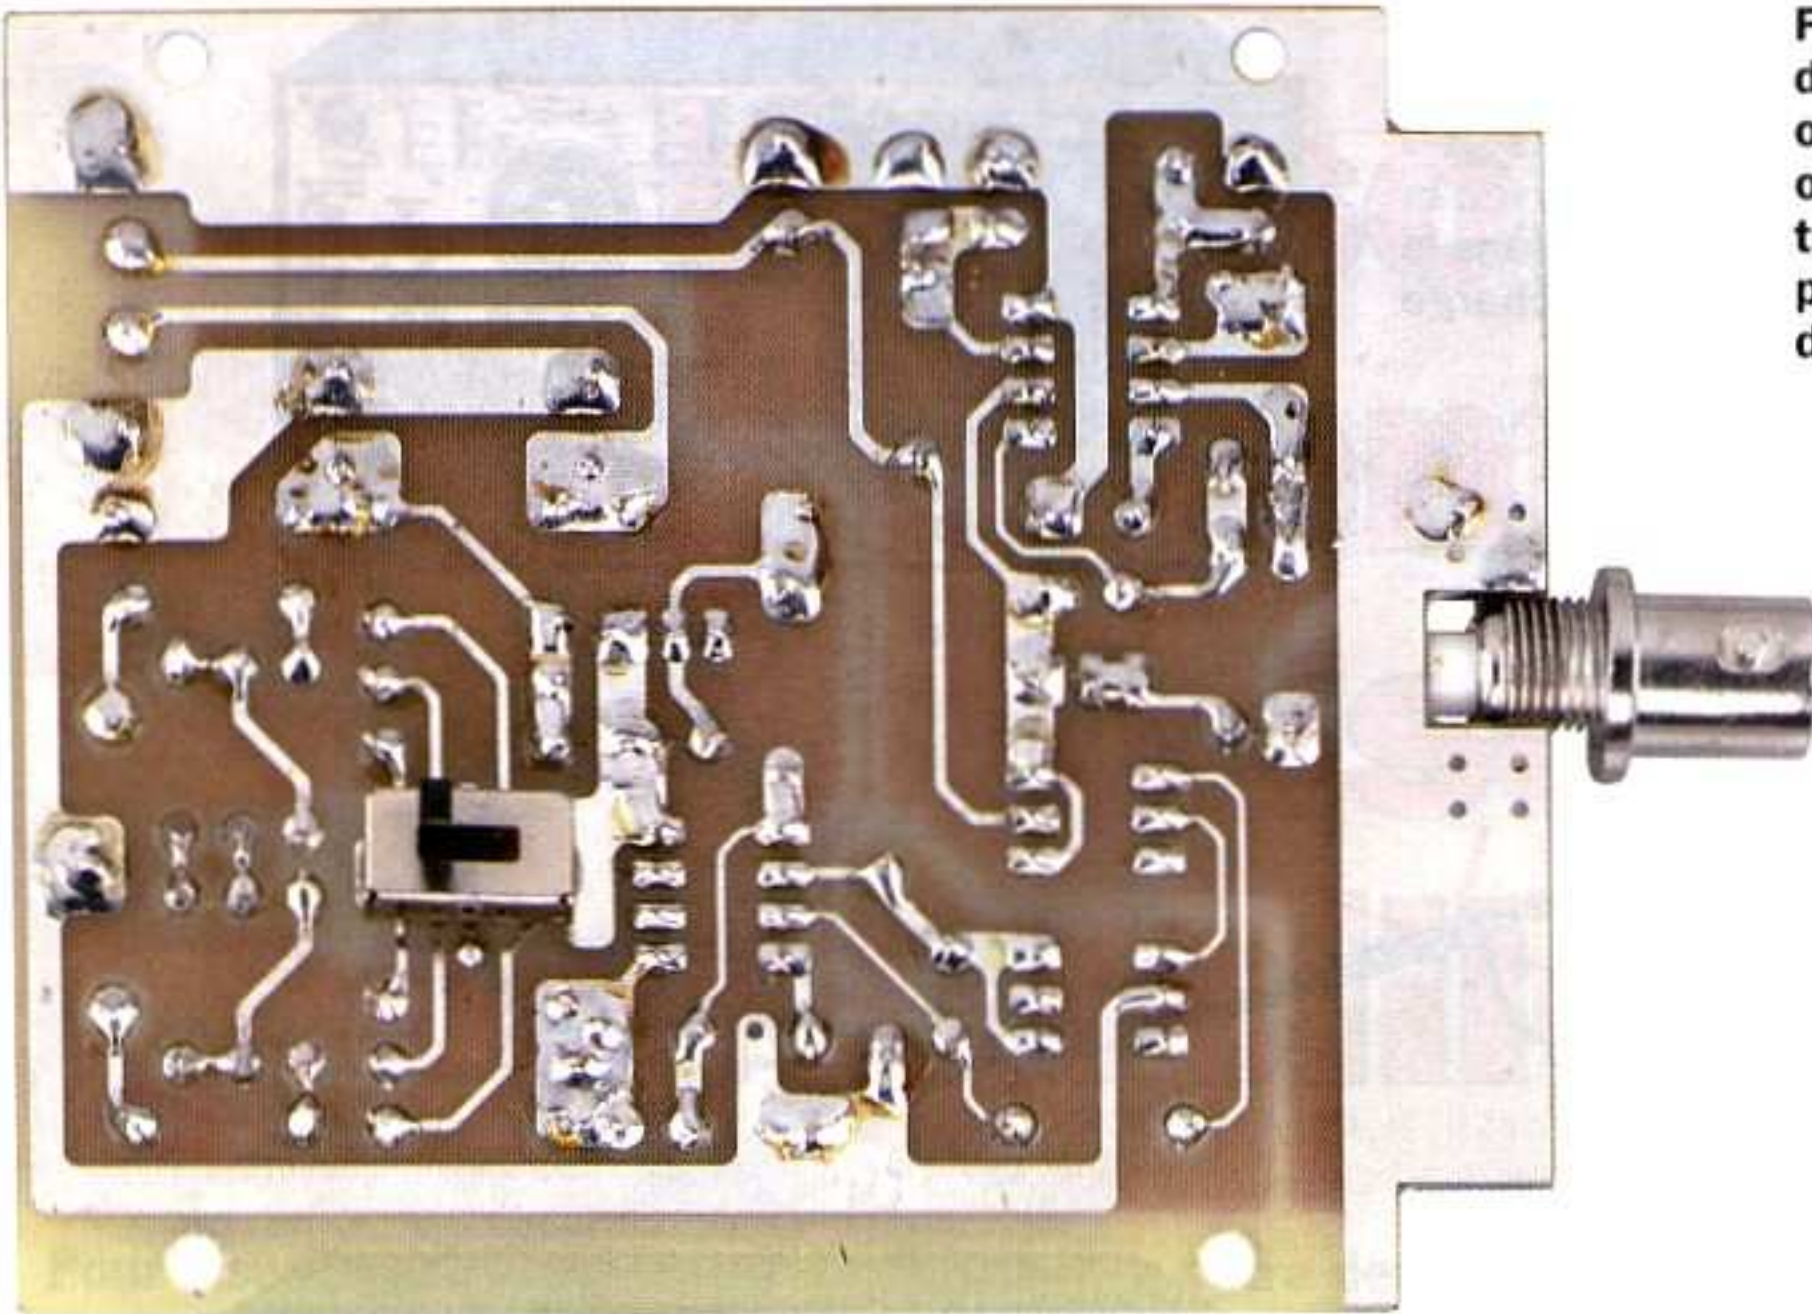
Photo d'un des prototypes de la platine de la sonde différentielle opto-isolée EN1707, vue côté soudures, où est monté l'inverseur à deux voies et trois positions (S2/A-S2/B, voir figure 6) permettant d'atténuer le signal d'entrée de 10, 100 ou 1 000 fois.
